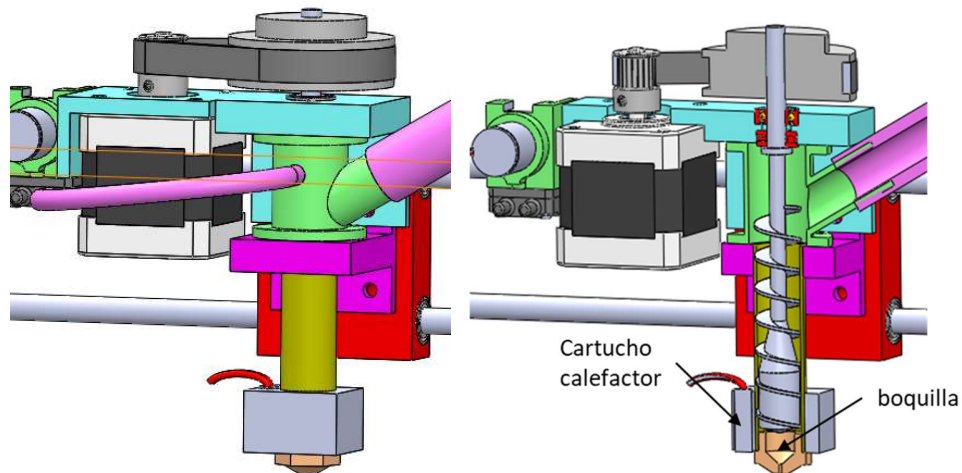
Montaje de bloque calentador, boquilla de extrusión y corte del ensamblaje
